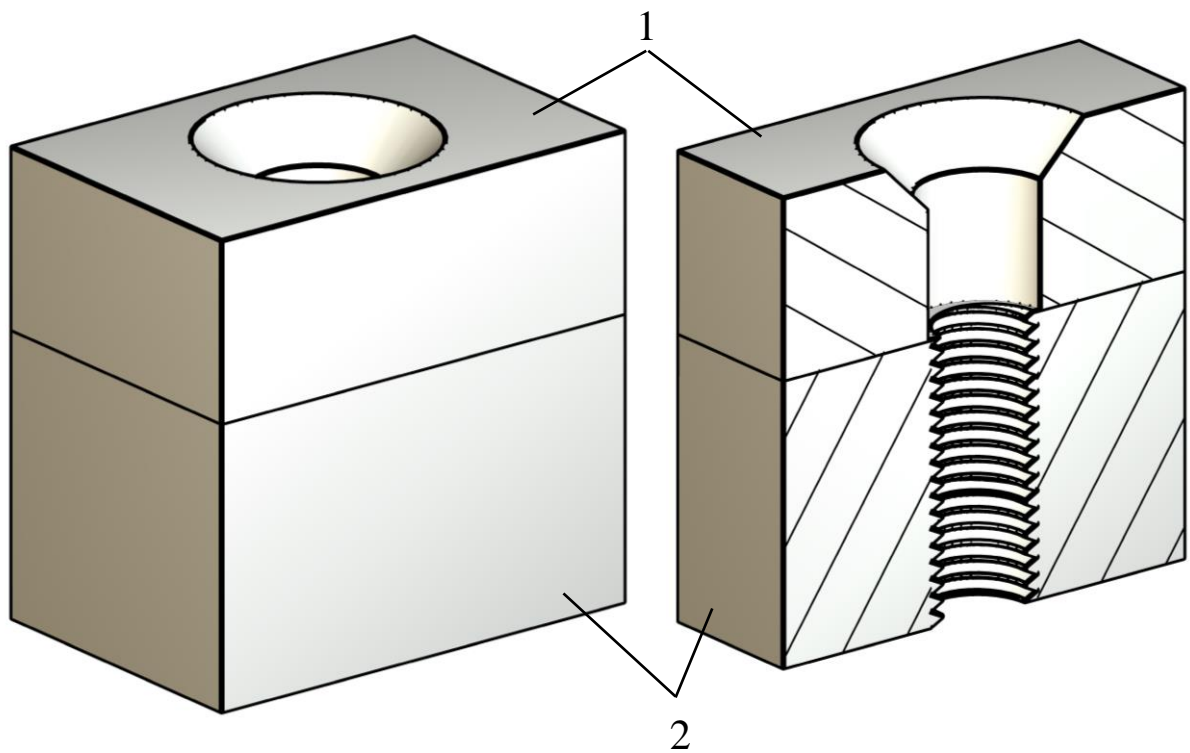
Детали, соединяемые посредством стандартного крепежного изделия – винта (справа изображение выполнено условно в разрезе): 1 – присоединяемая деталь с отверстием под винт и посадочным углублением (зенковкой) под головку винта; 2 – деталь с резьбовым отверстием
